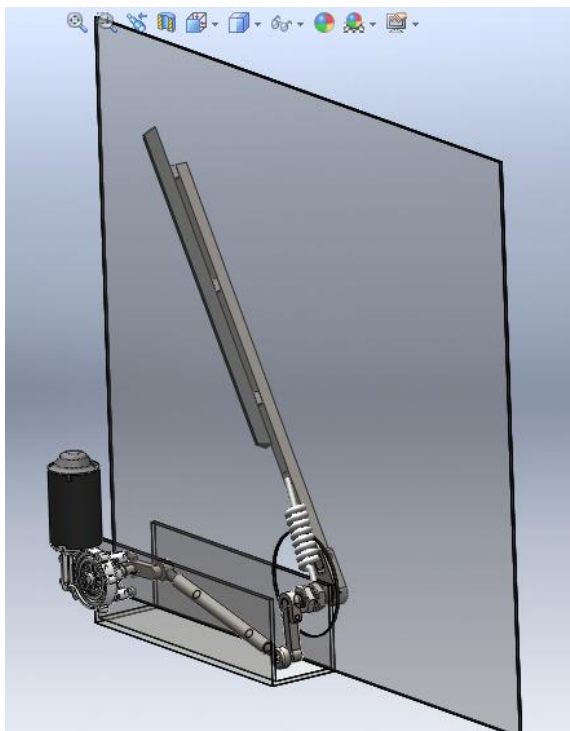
Desenho 3D do mecanismo de transmissão do limpador de para-brisas
